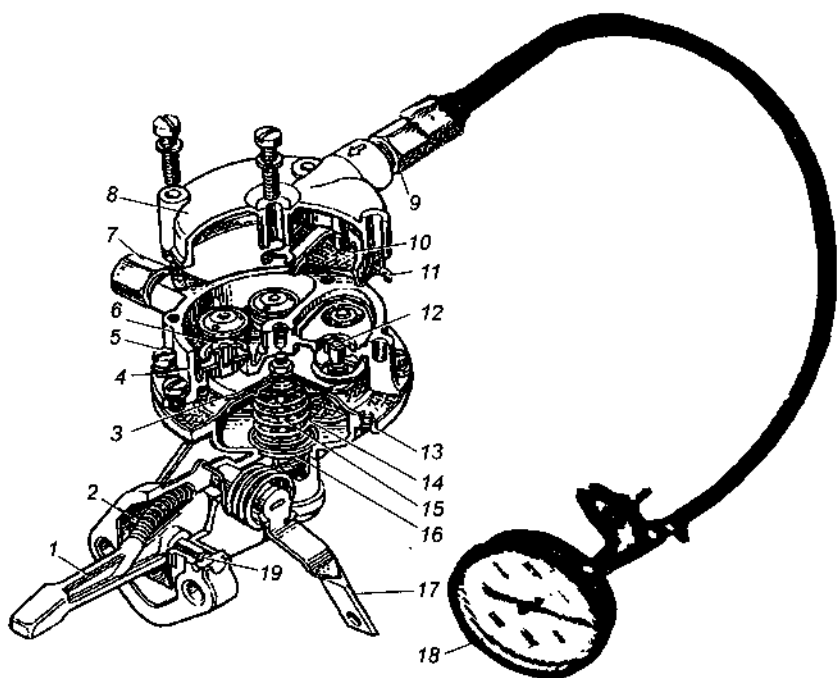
Бензонасос с вакуумметром: 1 — коромысло; 2 — возвратная пружина; 3 — мембрана; 4 — головка насоса; 5 — соединительный винт; 6 — выпускной клапан; 7 — штуцер для отвода топлива; 8 — крышка; 9 — штуцер для подвода топлива; 10 — сетчатый фильтр; 11 — резиновая прокладка; 12 — впускной клапан; 13 — корпус; 14 — пружина мембраны; 15 — толкатель; 16 — упорная шайба; 17 — рычаг для ручной подкачки топлива; 18 — вакуумметр; 19 — ось коромысла
